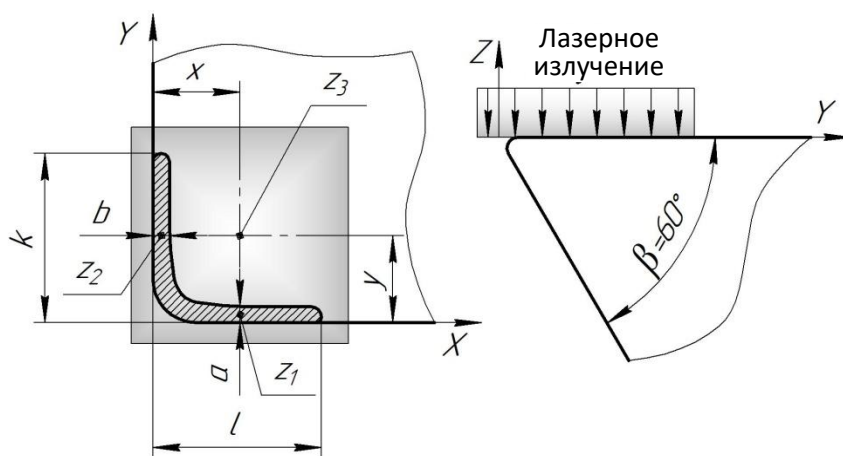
Расположения пятна лазерной обработки относительно вершины режущего клина инструмента и измеряемые параметры: l , a и k , b – длина и ширина упрочненной зоны вдоль главной и вспомогательной режущих кромок соответственно; z – глубина упрочненной зоны ($1, 2, 3$ – места замера глубины). Значения k и l определяют расстояние от начала системы координат до края упрочненной зоны на кромках режущего клина
